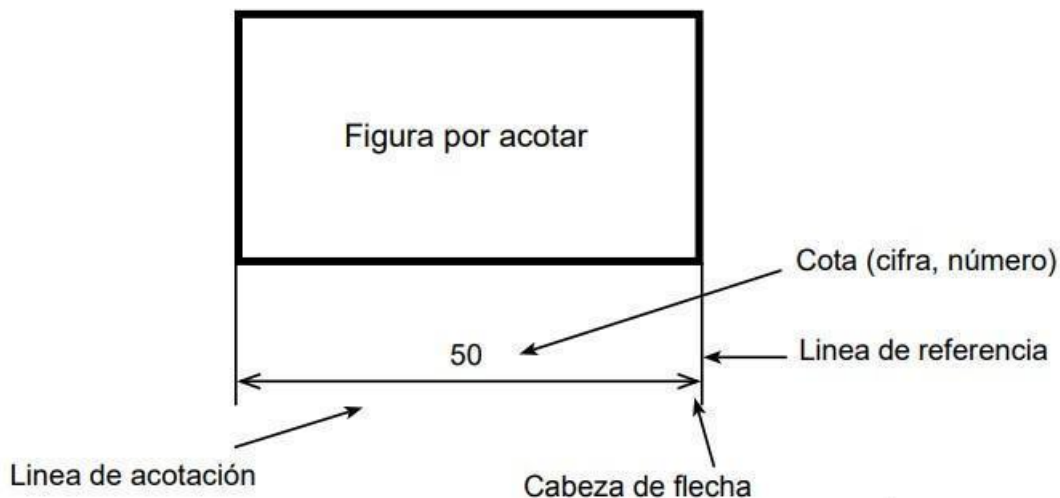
Figura IV. Elementos de un objeto acotado. *Dibujo Técnico I. Universidad de Sinaloa.
